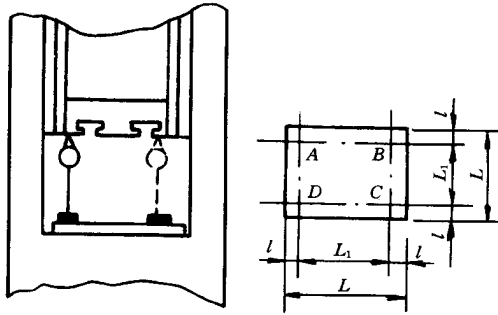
检验滑块下平面与工作台上平面的平行度
